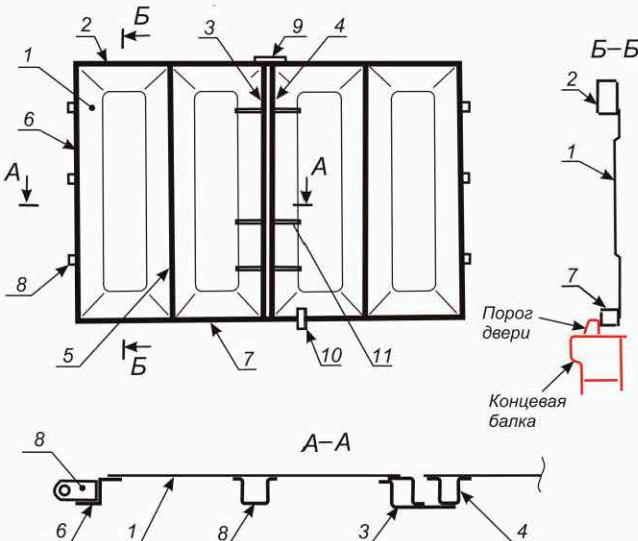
Схема торцевой двери полувагона модели 12-757:
